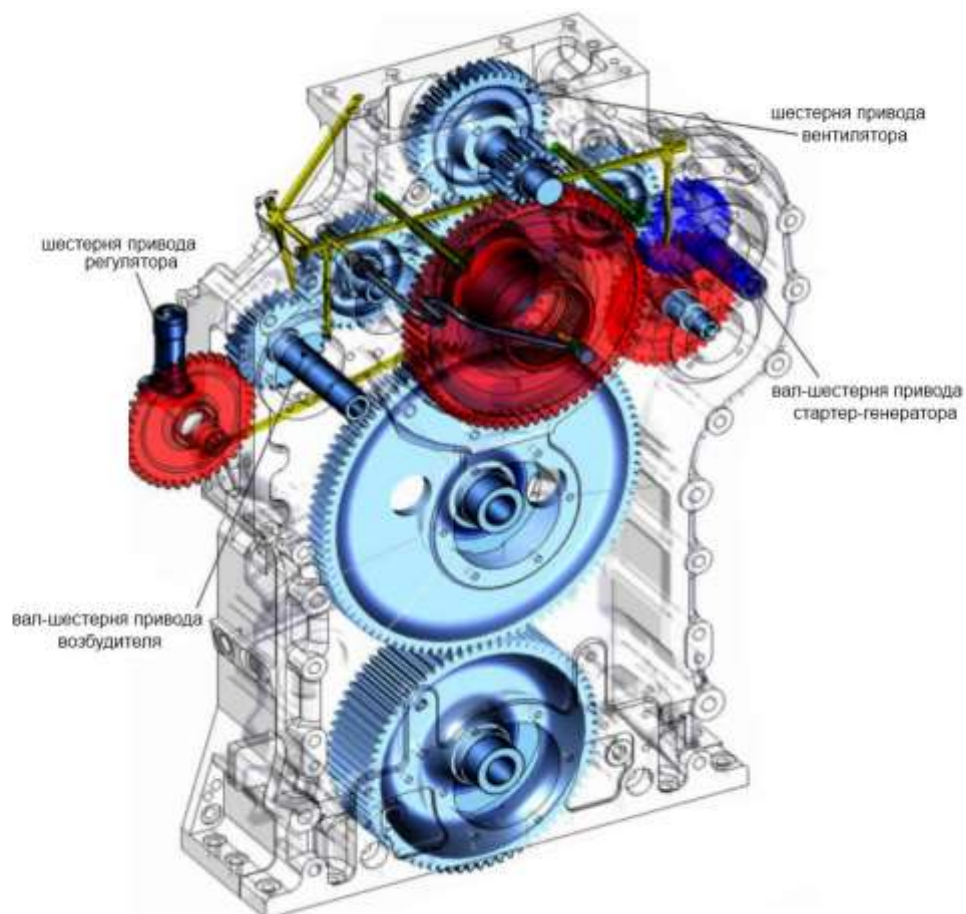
Кинематическая схема привода распределительного вала и смазки
